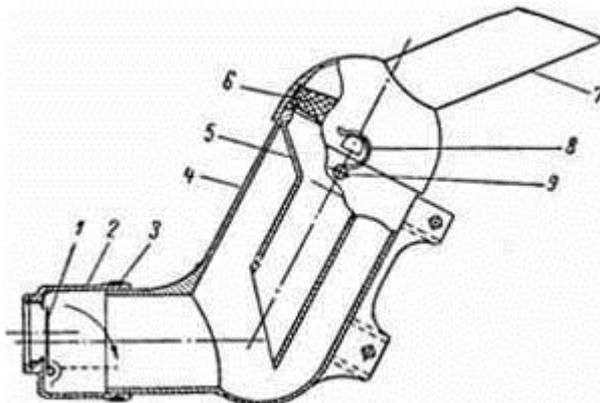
Разрез воздухофильтра с глушителем шума впуска:
